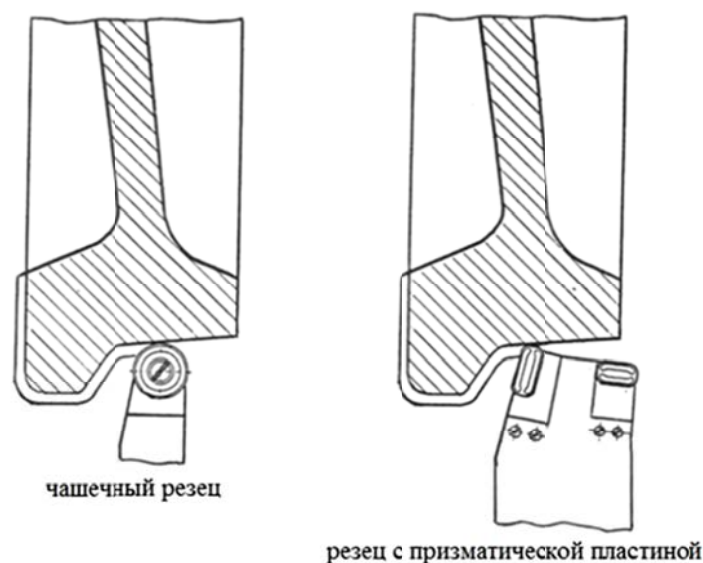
Пример обработки колесной пары сборными резцами
